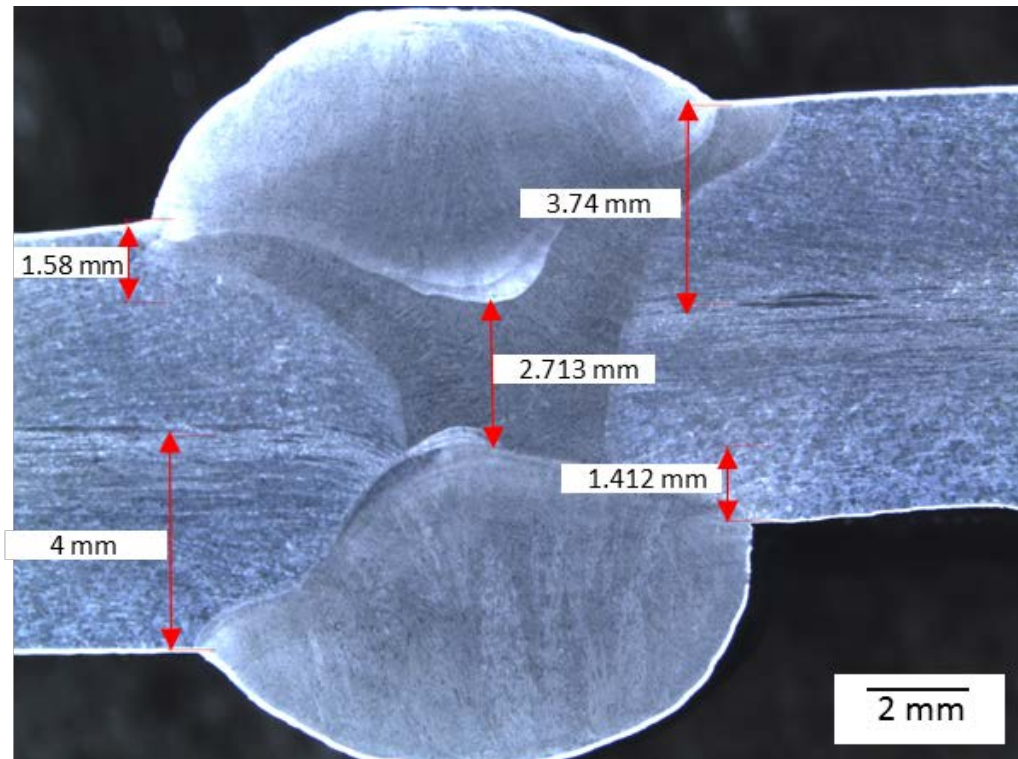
Imagen por macrografía óptica de la soldadura mostrando las características dimensionales.
